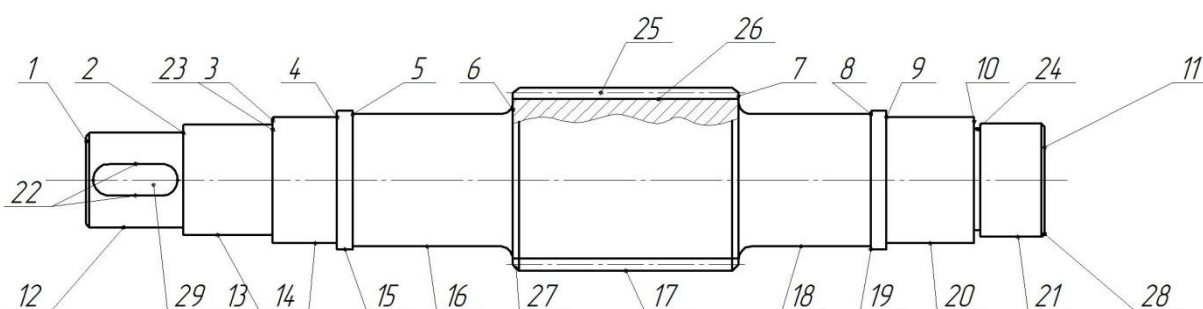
Схема с номерами поверхностей вал-шестерни
